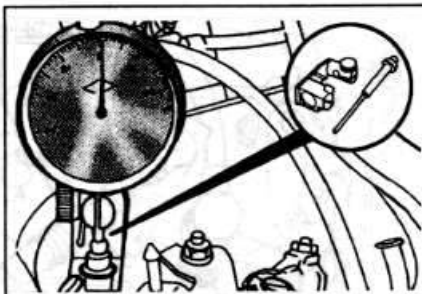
Установка ножки индикатора на внутреннюю ступеньку переходника на автомобилях выпуска с 1988 г.
